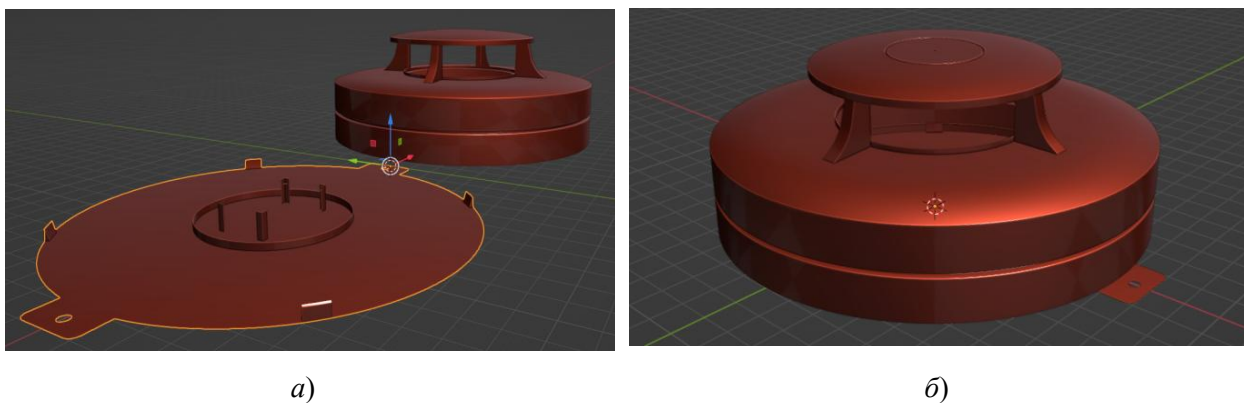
3D модель пожежного сповіщувача; а) корпусні деталі ПС, б) ПС в зібраному стані.
